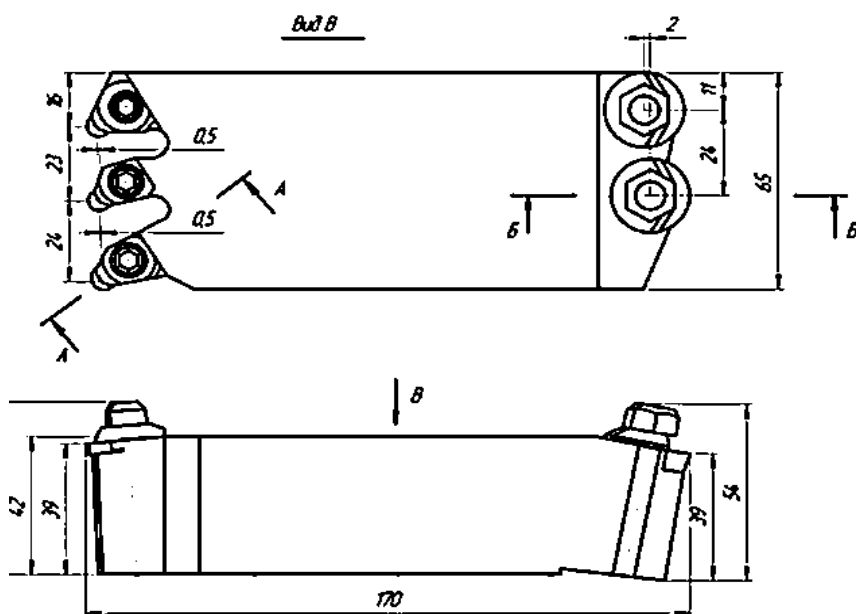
Комбинированный резец с круглыми пластинами из композита (слева) и ВК10ОМ (справа)
